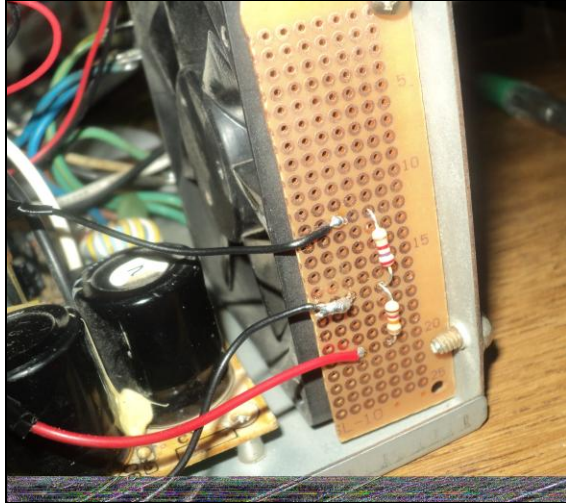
vista del divisor de tensión armado. (Fuente: propia)
